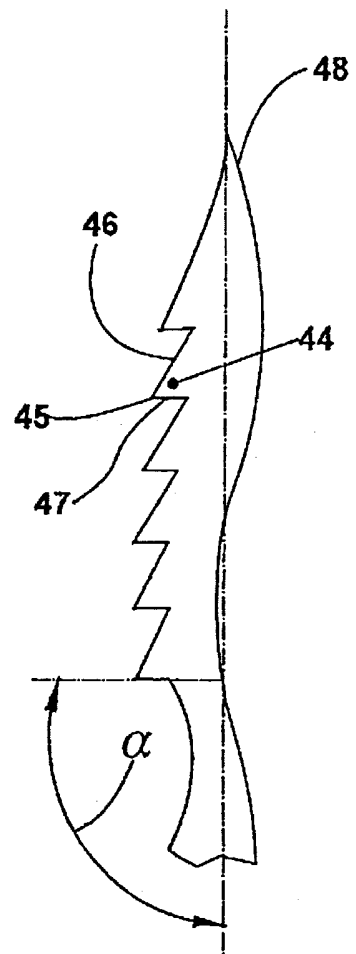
Obr. 4b Obr. 5a Obr. 5b
